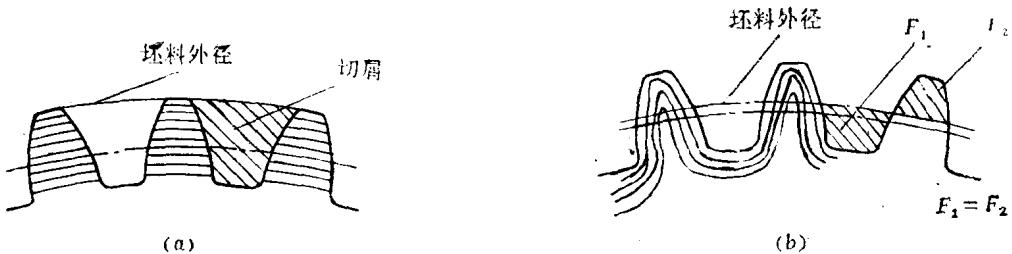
齿轮齿形部分的切削加工(a)与塑性加工(b)
